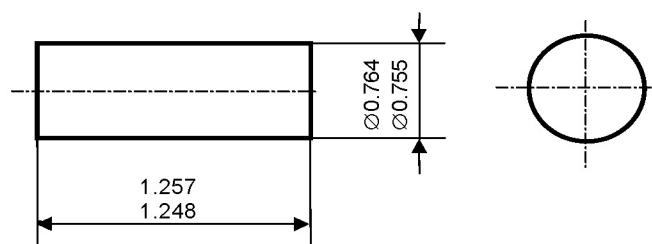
Dimensionado de una pieza cilíndrica con tolerancias dimensionales
